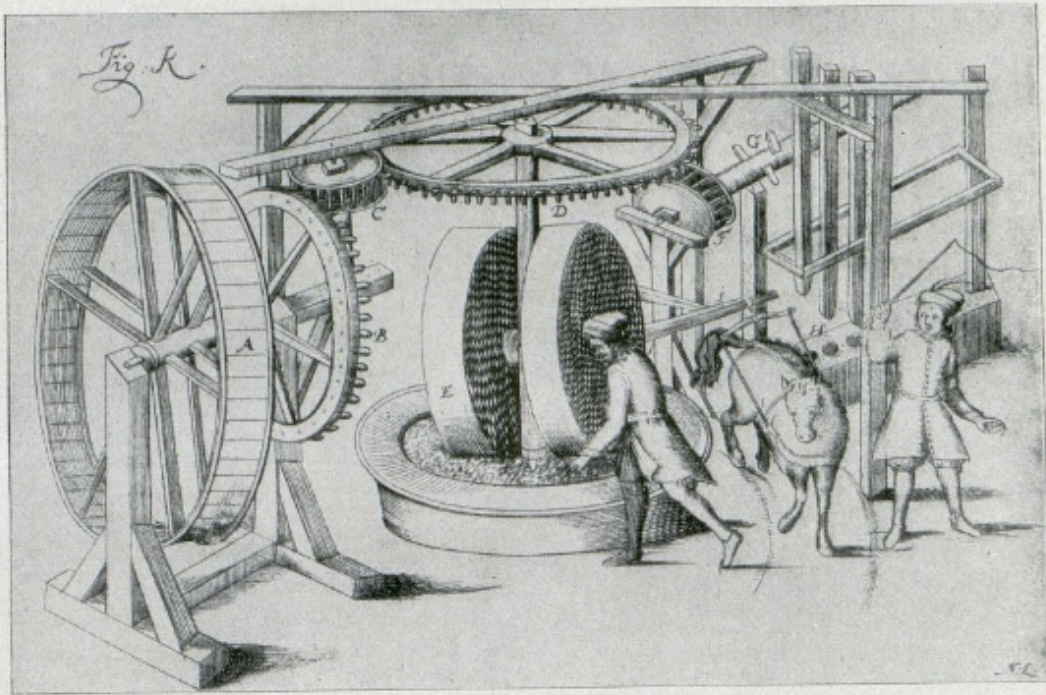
Pulvermühle und Stampfwerk mit Pferdebetrieb im 17. Jahrhundert
